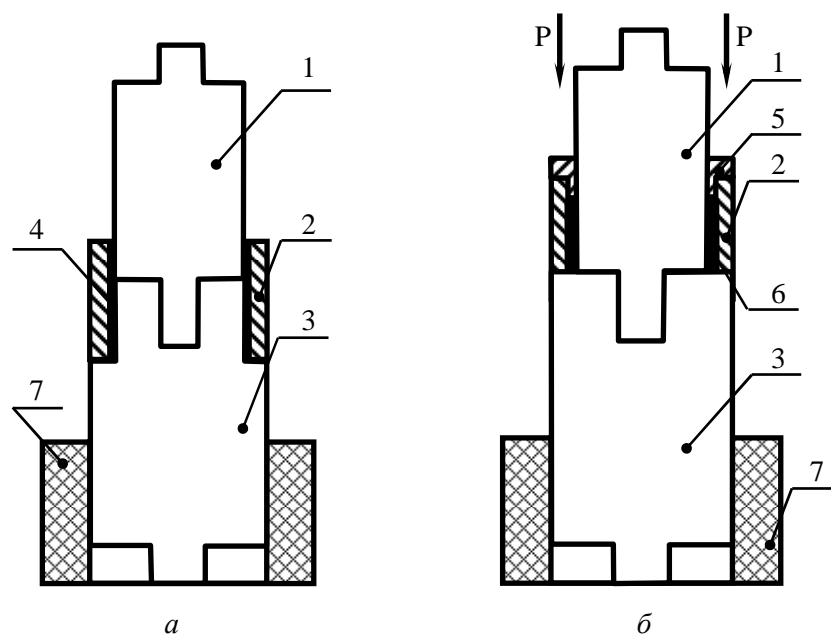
Схемы сборки металлокерамического сочленения типа “шип-паз” под пайку (а) и для сварки давлением (б): 1 — керамическая деталь; 2 — металлическая втулка; 3 — металлическая деталь; 4 — припой; 5 — прижимное кольцо; 6 — алюминиевая прокладка; 7 — графитовая оснастка
